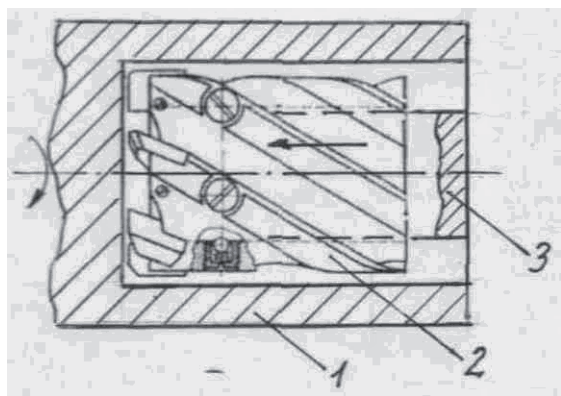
Сверление отверстий большого диаметра с использованием кольцевой резцовой головки: 1 – заготовка; 2 – кольцевая резцовая головка; 3 – высверливаемый стержень
